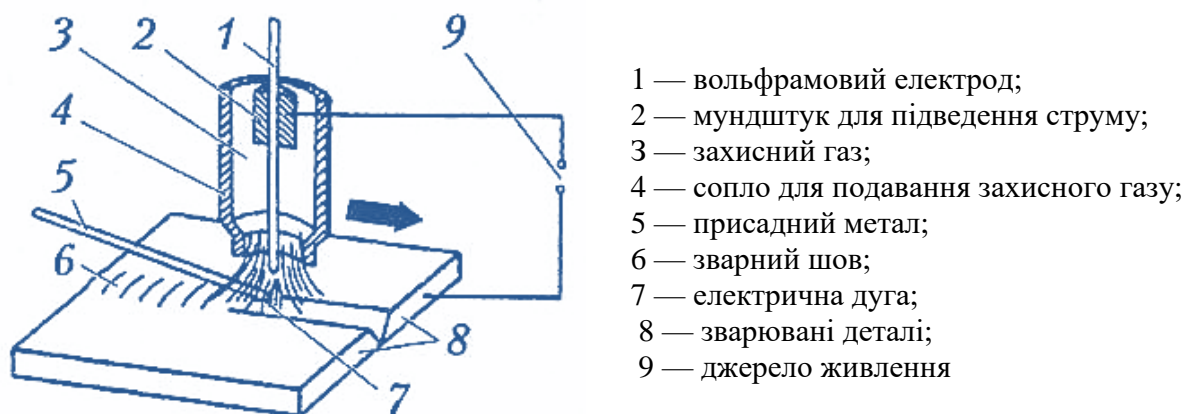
Схема аргоно-дугового зварювання [6]
